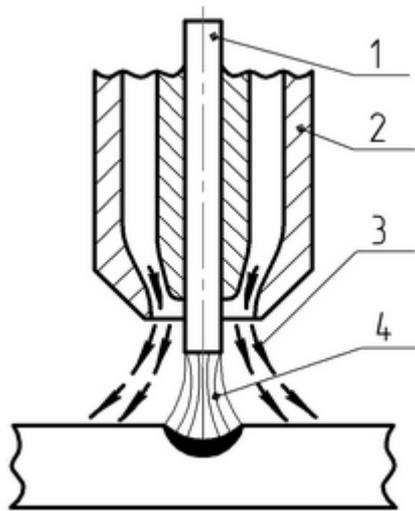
Схема процесса сварки в защитной среде защитного газа: 1 – сварочная проволока; 2 – горелка; 3 – струя защитного газа; 4 – дуга
